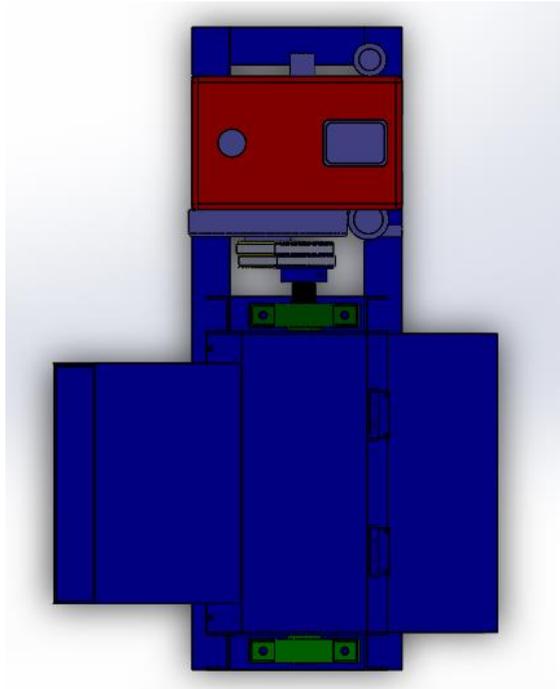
Mesin Pencacah Pelepah Sawit Berkapasitas 90Kg/Jam Pandangan Depan
